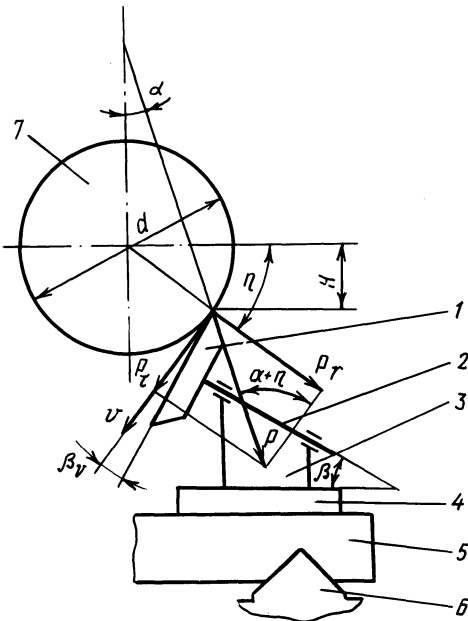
Схема установки роторного реза на универсальном токарном станке
